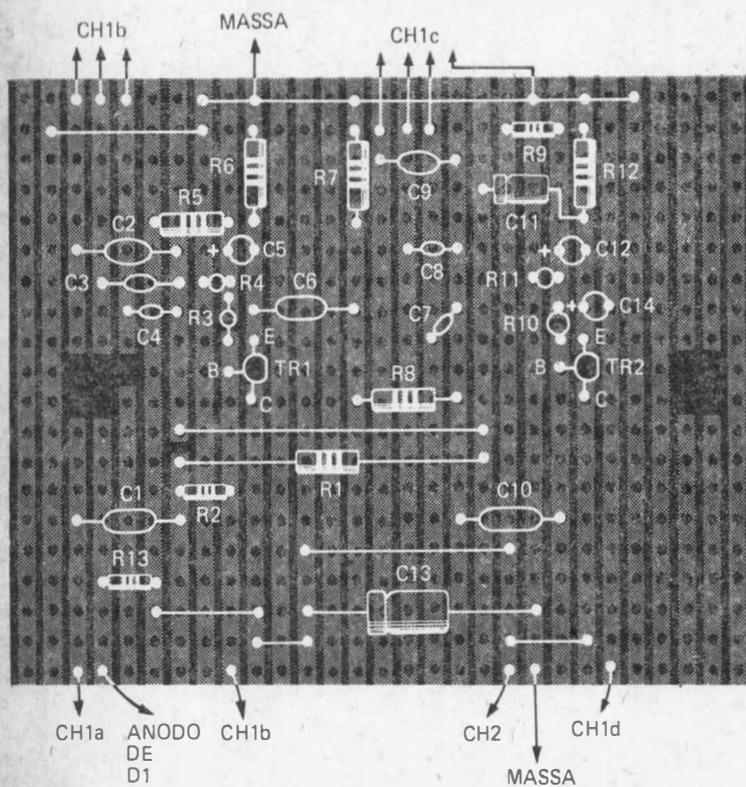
Arranjo dos componentes sobre a plaqueta da Fig. 3.
